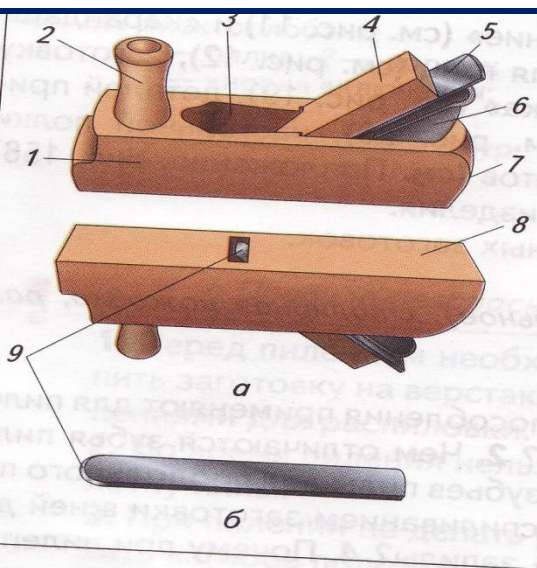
Шерхебель: *а* — общий вид: 1 — колодка; 2 — рукоятка; 3 — леток; 4 — клин; 5 — нож; 6 — упор; 7 — пятка; 8 — подошва; 9 — лезвие; б — нож
